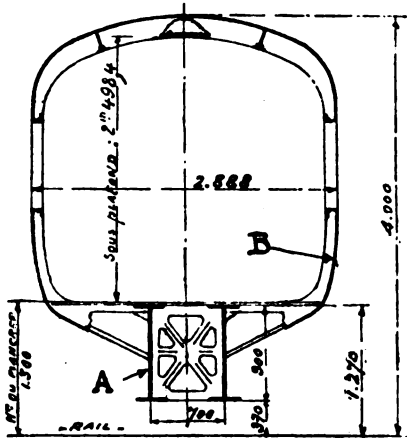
Sezione trasversale delle carrozze: A) trave in acciaio; B) cassa tubulare in alluminio.
